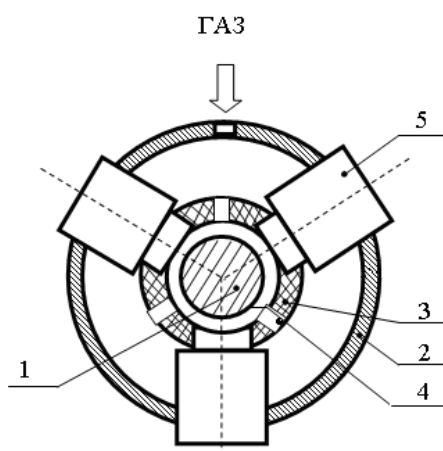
Конструктивная схема газоманнитного подшипника:
